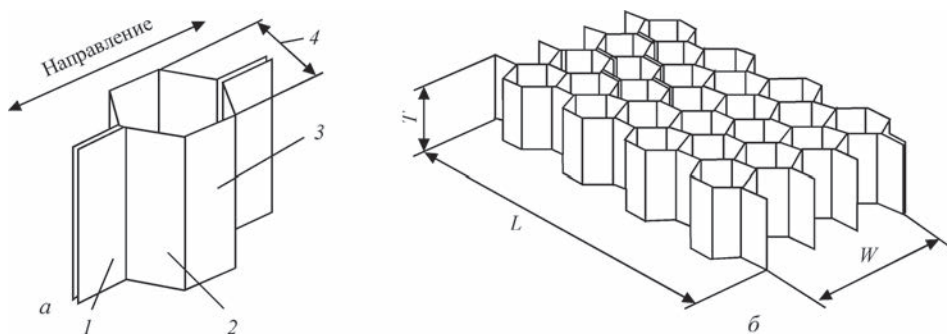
Сотовый наполнитель с шестигранной формой ячеек: а — вид единичной ячейки (1 — гофрированные полосы; 2 — грани ячейки одинарной толщины; 3 — грани ячейки двойной толщины; 4 — размер ячейки); б — основные параметры сотового наполнителя (L — длина, T — толщина, W — ширина) [8]
